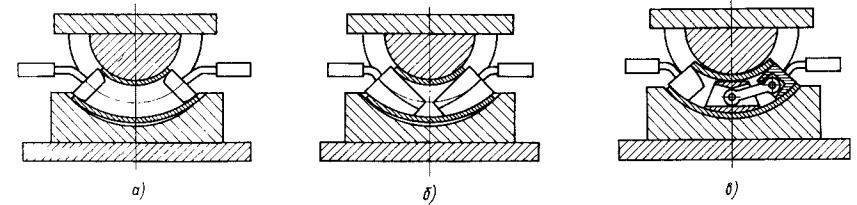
Схема штампа для гибки короткой трубы с введением оправок: а — с короткими цилиндрическими оправками; б — с ложкообразными (торoidalными) оправками; в — с шарнирной (справа) и простой (слева) оправками
